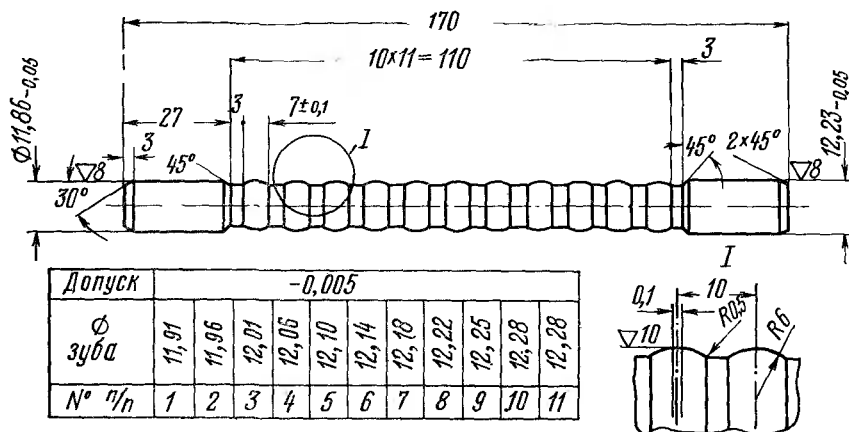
Брошь для обработки втулки верхней головки шатуна компрессора
